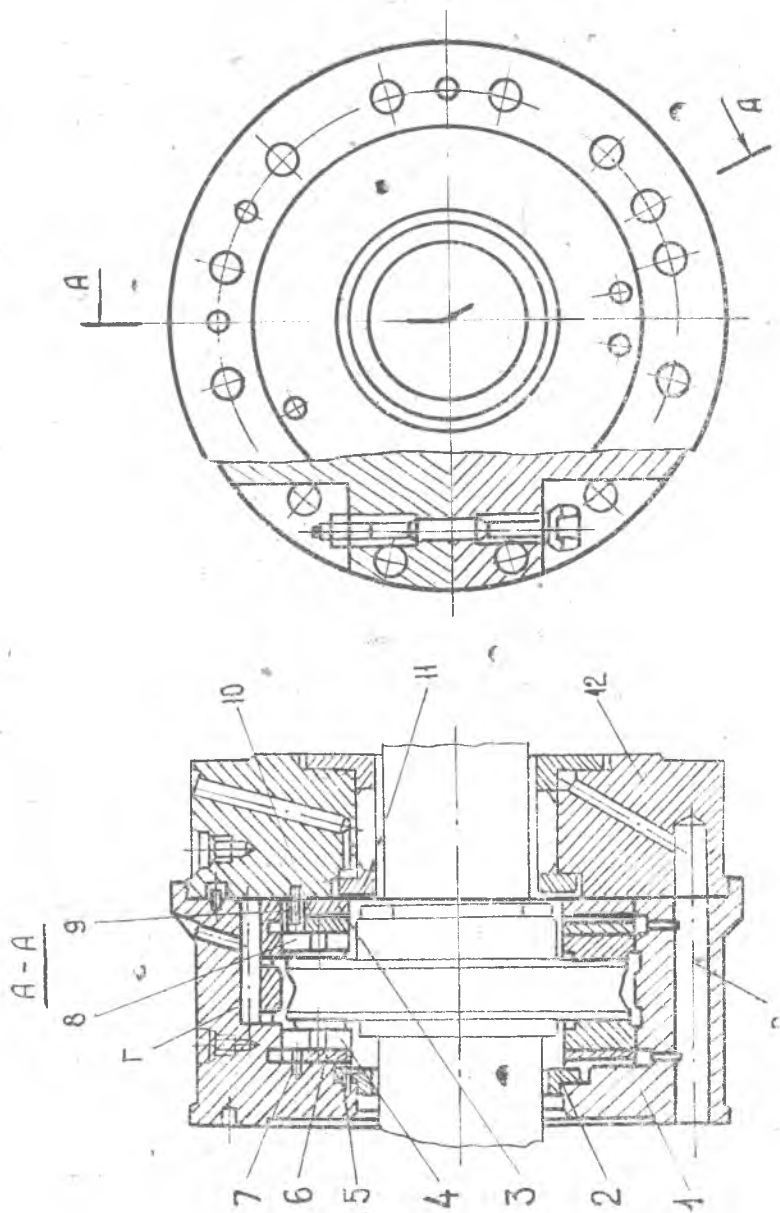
Подшипник опорно-упорный: 1, 12 — корпус; 2, 11 — втулка; 3 — кольцо регулировочное; 4, 8 — колодки упорные; 5 — винт; 6, 10 — кольцо несущее; 7, 9 — штифты
